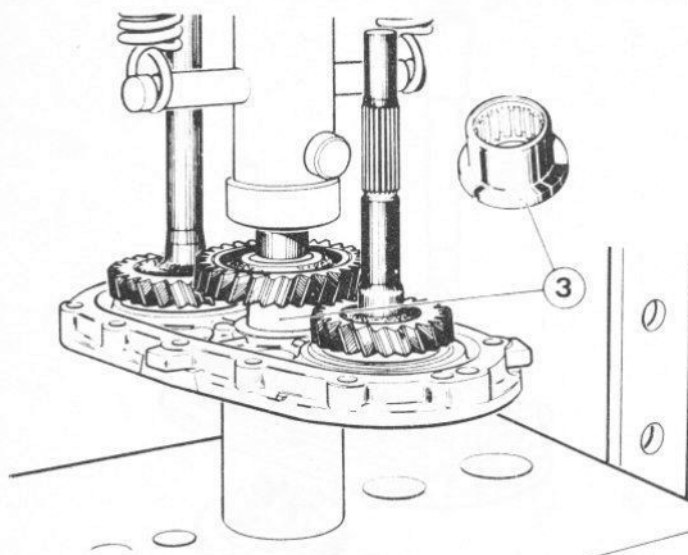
Arbre intermédiaire utilisé pour presser le roulement à aiguilles (3) dans la plaque intermédiaire (Sec 9)
